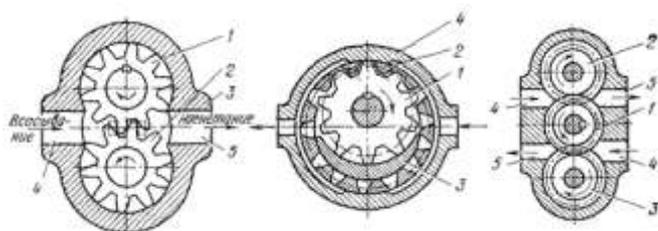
Схемы шестеренных насосов: а - с внешним зацеплением; б - с внутренним зацеплением; в - трехшестеренный
